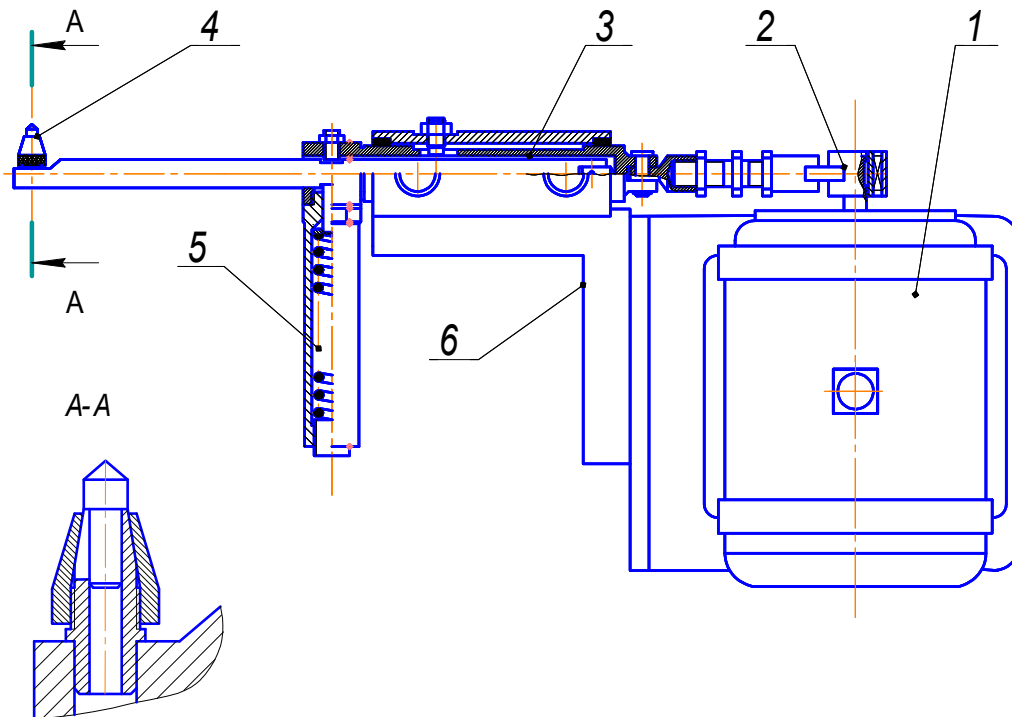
Конструктивна схема обладнання для вібраційного обкочення
